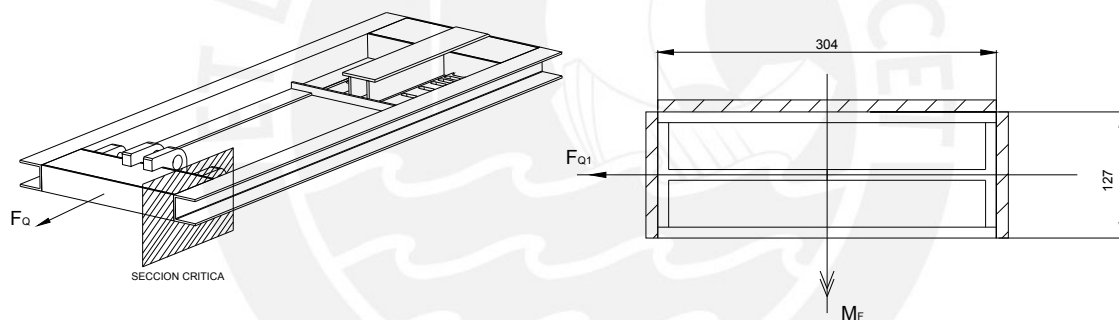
SECCION CRITICA DE SOLDADURA EN LA PLATAFORMA INFERIOR
